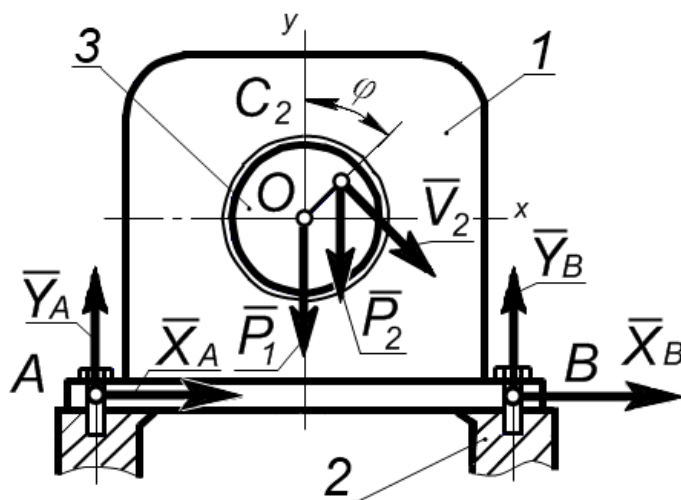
Розрахункова схема для визначення вертикального тиску та горизонтальних зусиль у болтових з'єднаннях коробки швидкостей з передньою тумбою
